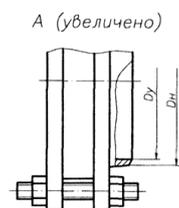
Габаритные размеры и конструкция МИЖУ:
